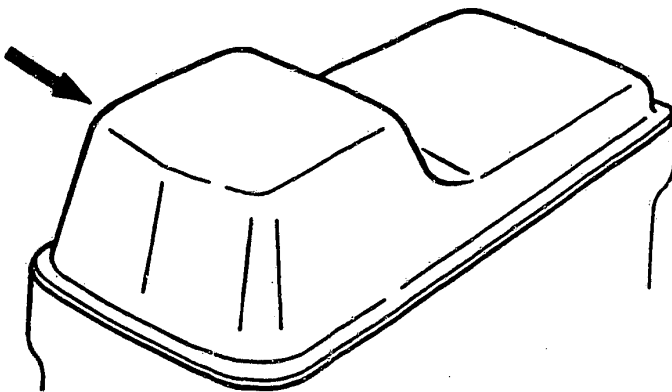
Beim Ausbau der Ölwanne ist mit einem Hammer gegen die untere Ecke zu klopfen, nachdem die Schrauben entfernt sind. Durch Abdrücken der Ölwanne mit einem Schraubenzieher könnte sie beschädigt werden.
